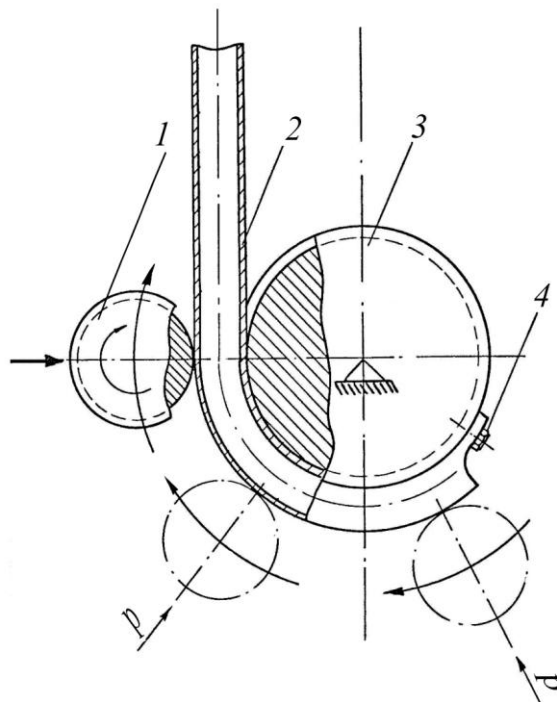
Принципиальная схема изготовления элементов привода: 1 – подвижный ролик, 2 – неподвижный ролик, 4 – фиксирующий винт
